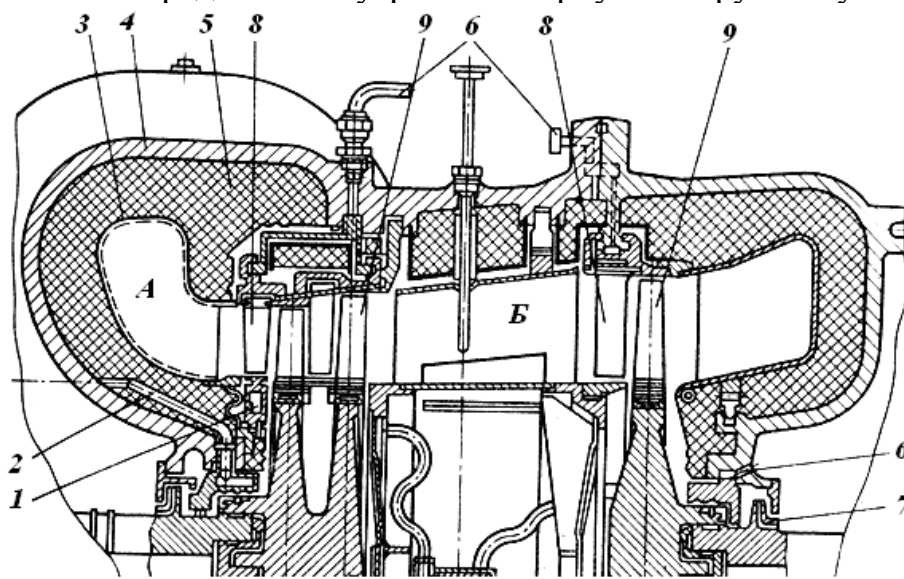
Газовая турбина установки ГТ-700-5 НЗЛ:
